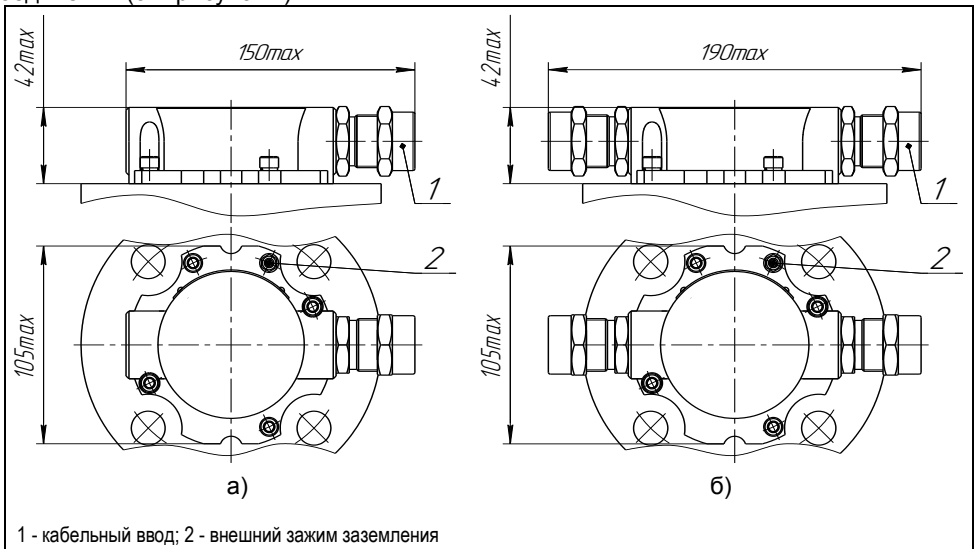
Варианты исполнения корпуса из алюминиевого сплава:
